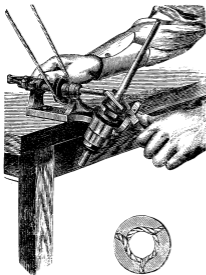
Drehbank oder Bohrmaschine. Fig. 4 Querschnitt der Hölzungen. Spulen in Spinnereien.
